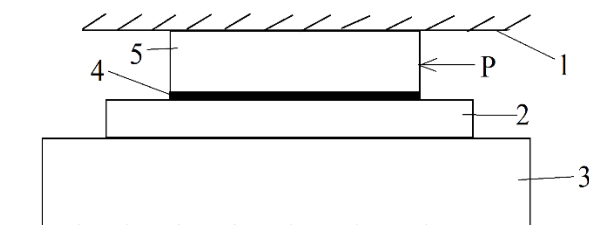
1 – корпус насоса; 2 – металлокерамическая втулка; 3 – вал; 4 – смазочный материал; 5 – сальниковая набивка
